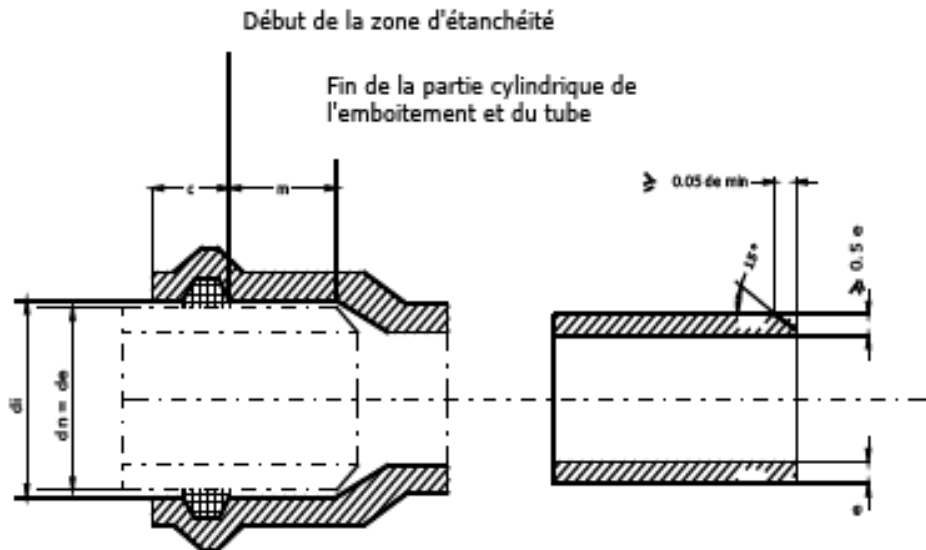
Emboîtement des tubes pour assemblages du type à bague d'étanchéité
